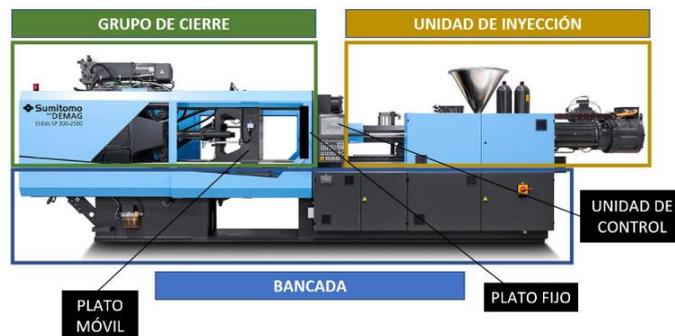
Máquina inyectora. Extraído de total-manufacturing.com
